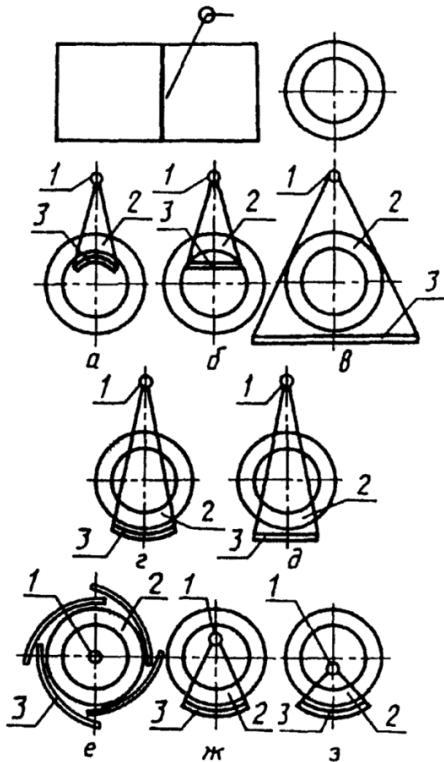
Схемы контроля сварных соединений кольцевых, цилиндрических и сферических пустотелых изделий: 1 – источник излучения; 2 – контролируемый участок; 3 – кассета с пленкой
